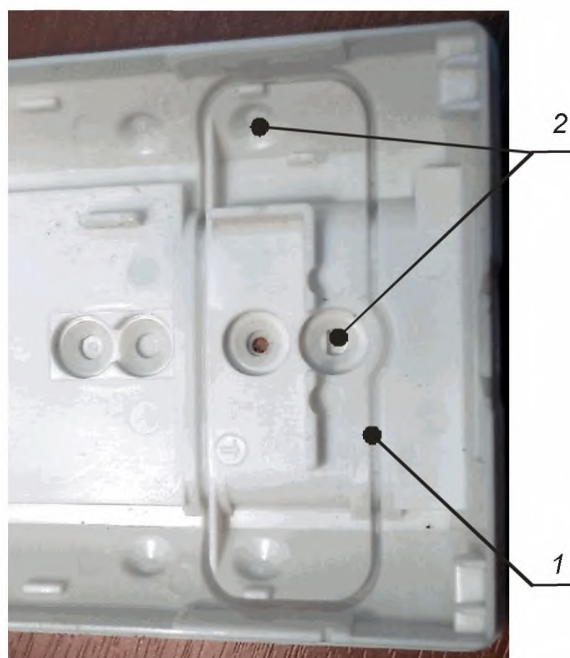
средство обнаружения отрыва корпуса извещателя
